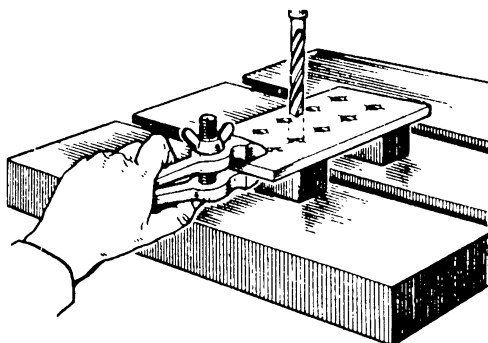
Закрепление детали в ручных тисках при сверлении
